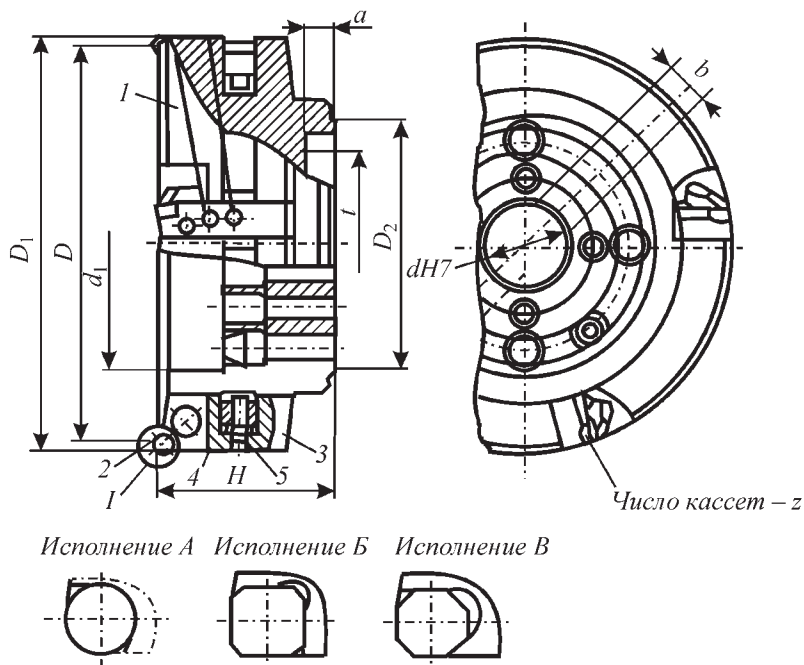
Торцовая фреза с механическим креплением режущих пластин
